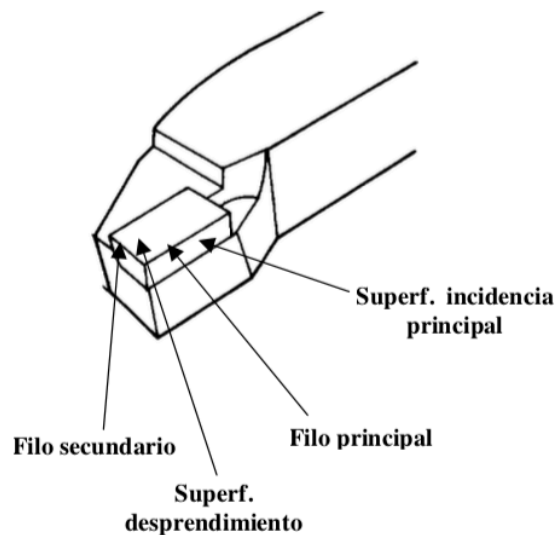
Filos de una herramienta de torneado [24, p. 3]
